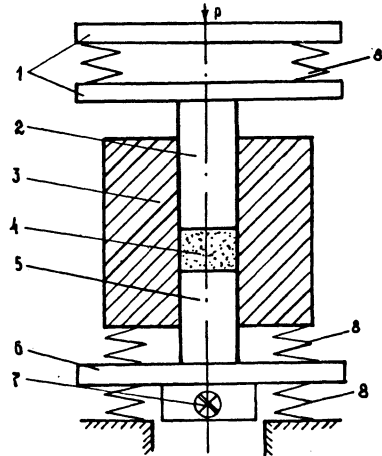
Схема вибрационного прессования: 1 - плиты; 2 - верхний пуансон; 3 - матрица; 4 - прессовка; 5 - нижний пуансон; 6 - опорная плита; 7 - вибратор; 8 - пружины
